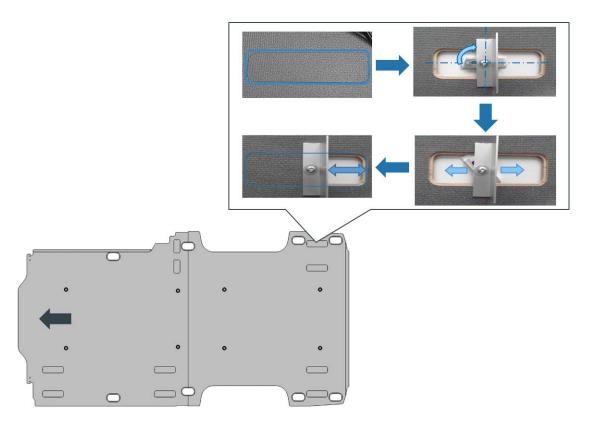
plancher universel, points de fixation pour systèmes d'armoires et d'étagères (ici, empattement L3 de 3 640 mm avec porte coulissante droite)
